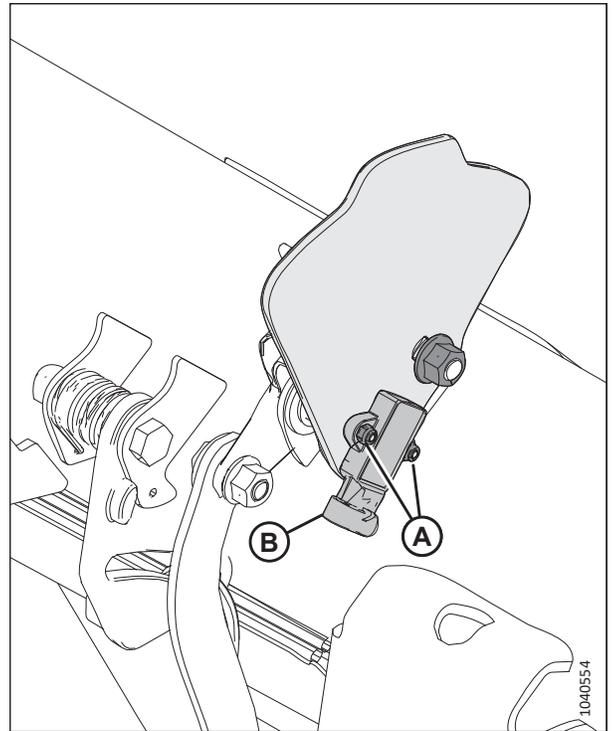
Linke Platte der Auflagedruckanzeige
